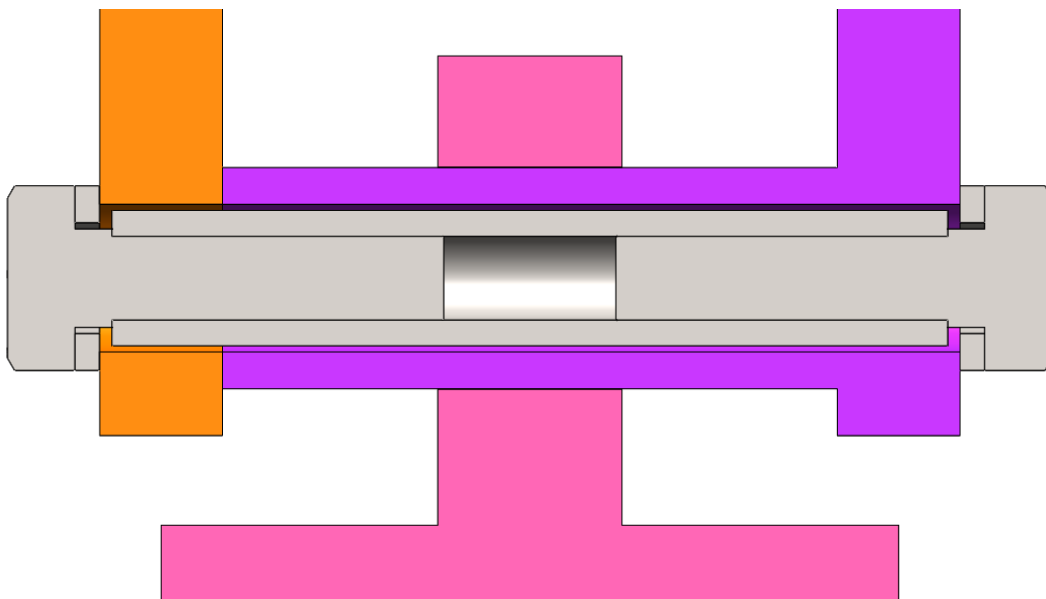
Vista de sección del amarre del cuerpo de las poleas fijas con el carrete (Fuente 36)
